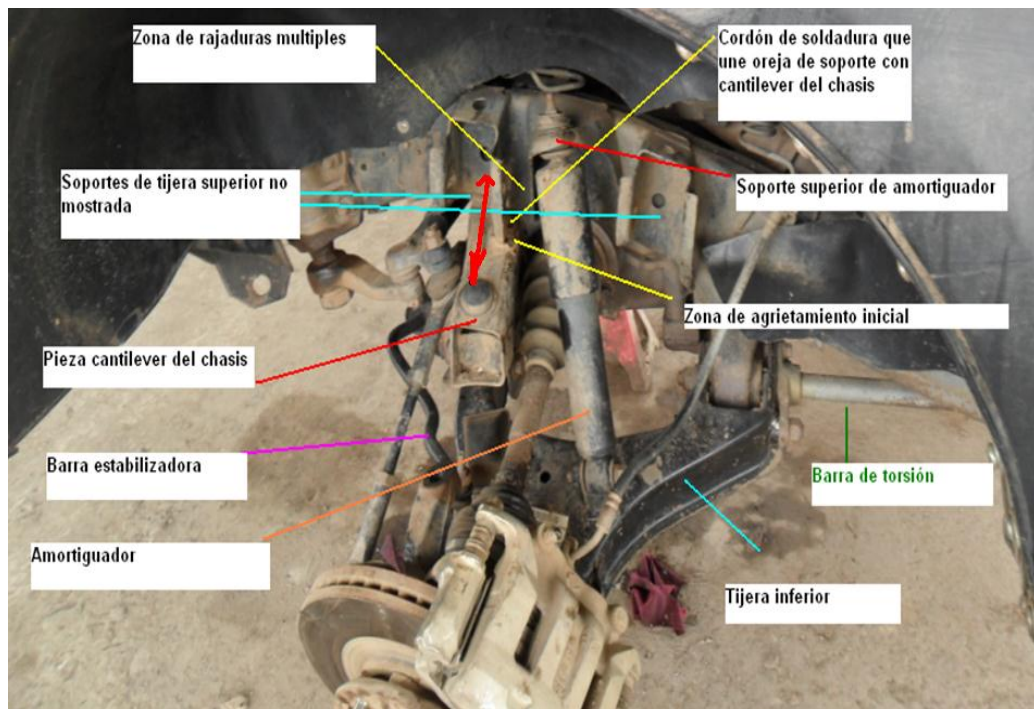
Cordón de soldadura donde se presenta el problema de las grietas.
